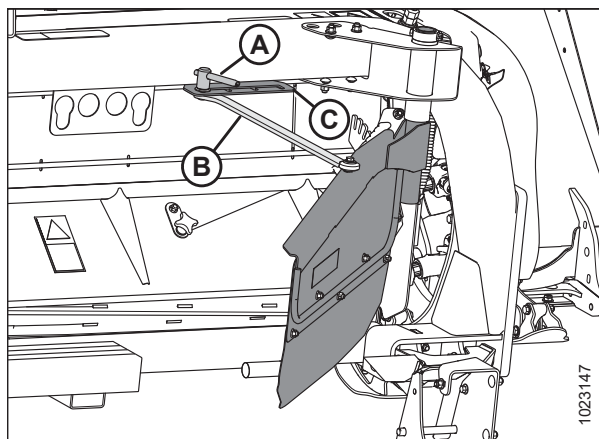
Боковой дефлектор формовочного щитка и регулировочная планка
